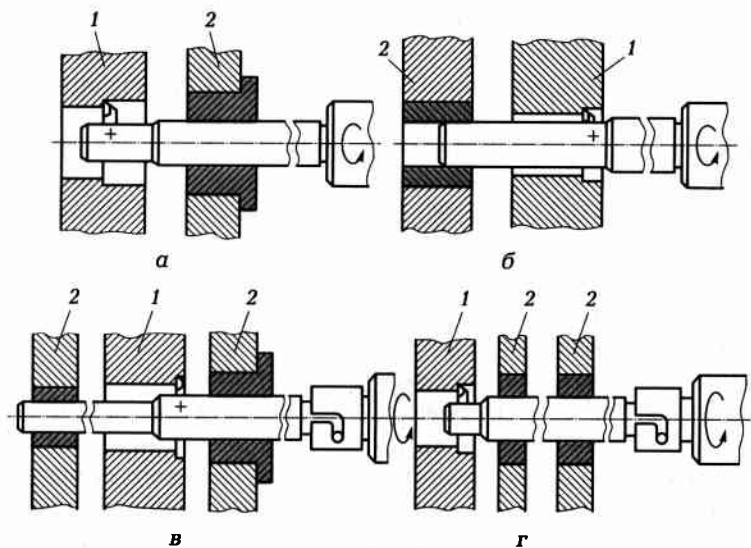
Расположение направляющих элементов приспособлений для растачивания отверстий:
